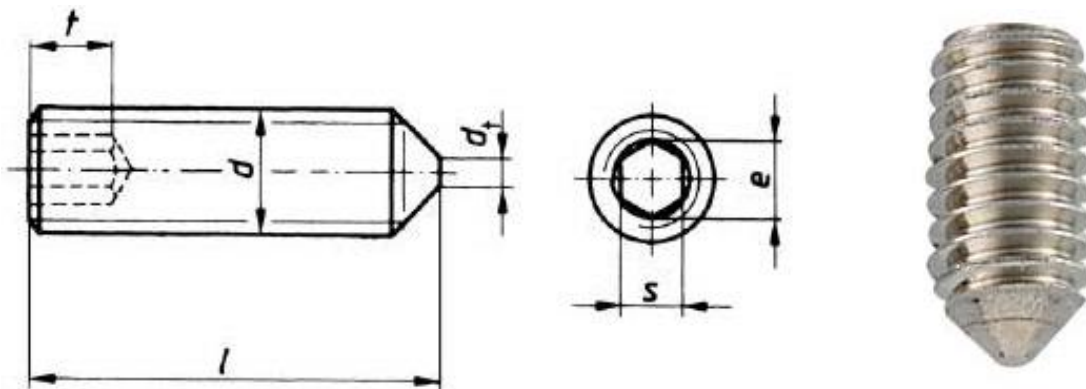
Gewindestift/Wurmschraube mit Innensechskant [23]
